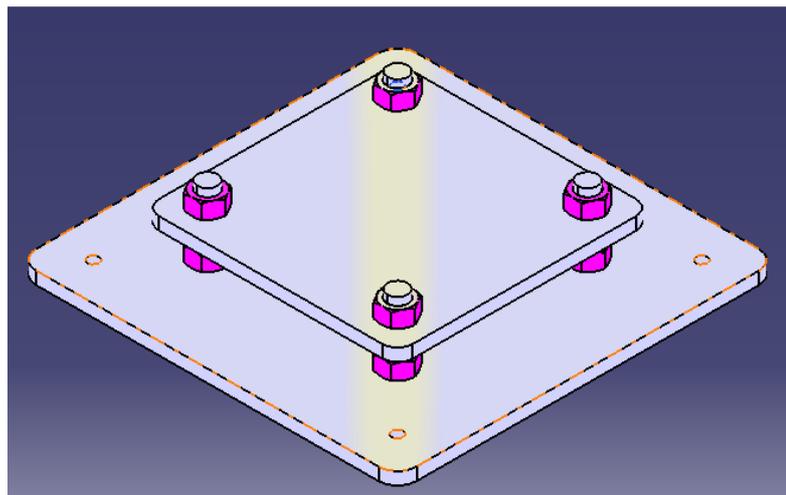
Anclaje de pilares de la plataforma atornillada donde confluyen los pilares.
